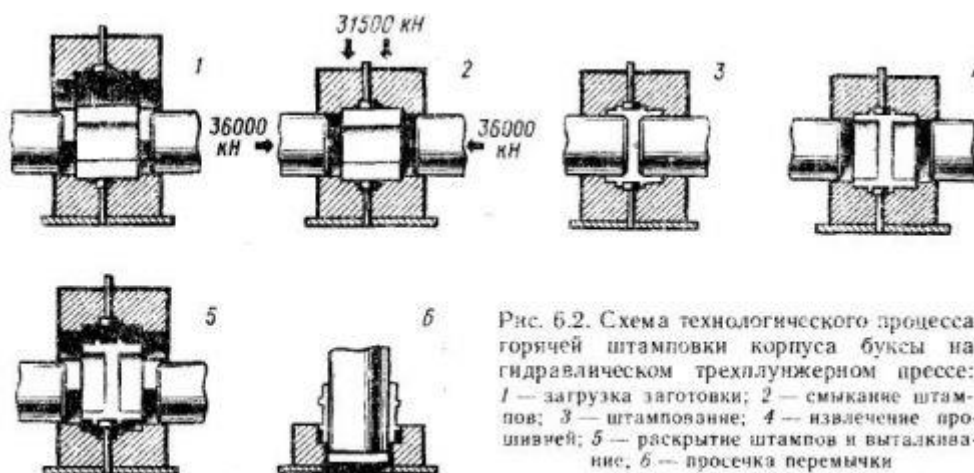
Схема технологического процесса горячей штамповки корпуса буксы на гидравлическом трехплунжерном прессе: 1 — загрузка заготовки; 2 — смыкание штампов; 3 — штампование; 4 — извлечение прошивной; 5 — раскрытие штампов и выталкивание; 6 — просечка перемычки
